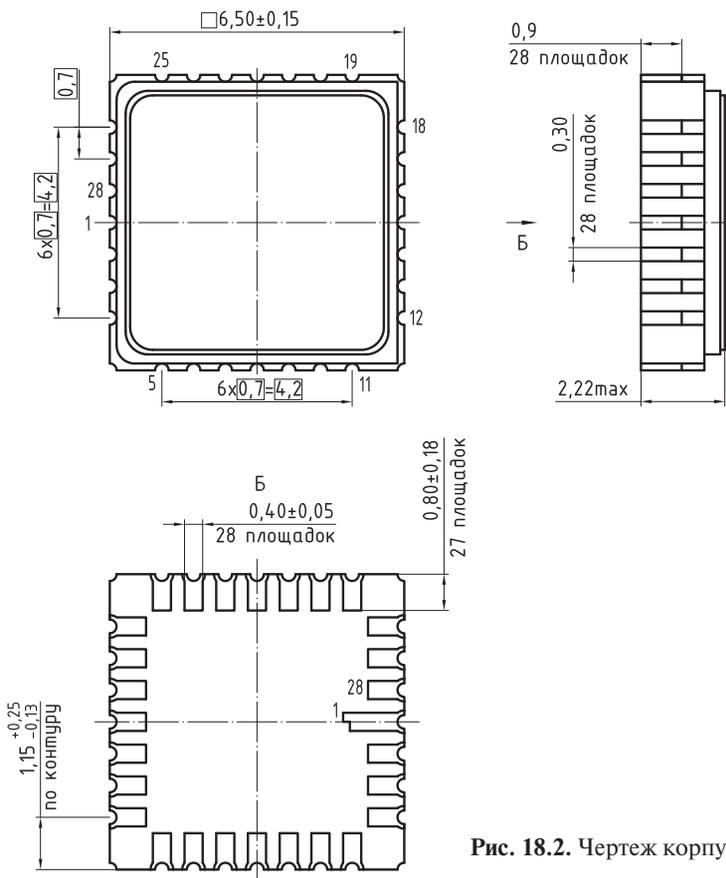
Чертеж корпуса МК 5123.28-1.01
